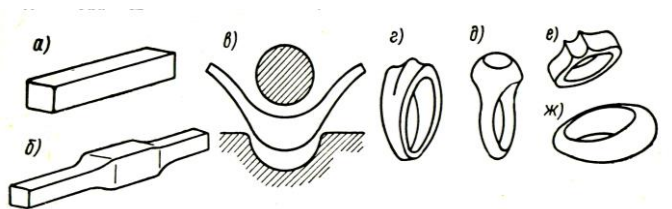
Переходыковки обручальных колец: а – заготовка штабик; б – провальцованная развертка заготовки кольца; в – гибка заготовки на свинцовой плите; г – ж – различные окончательные формы колец [6]
